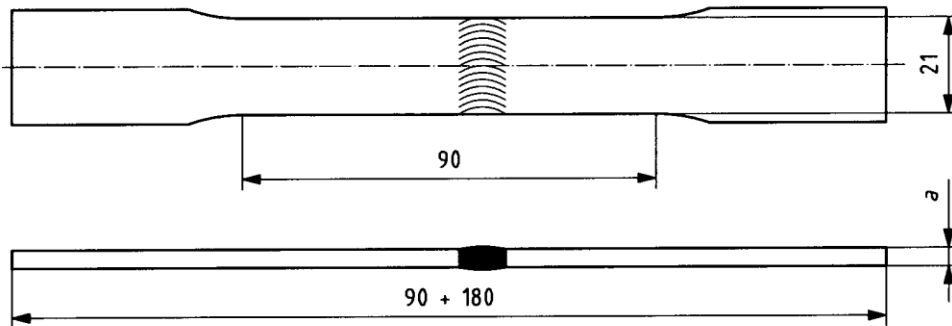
Probetas para el ensayo de tracción perpendicular a la soldadura.
